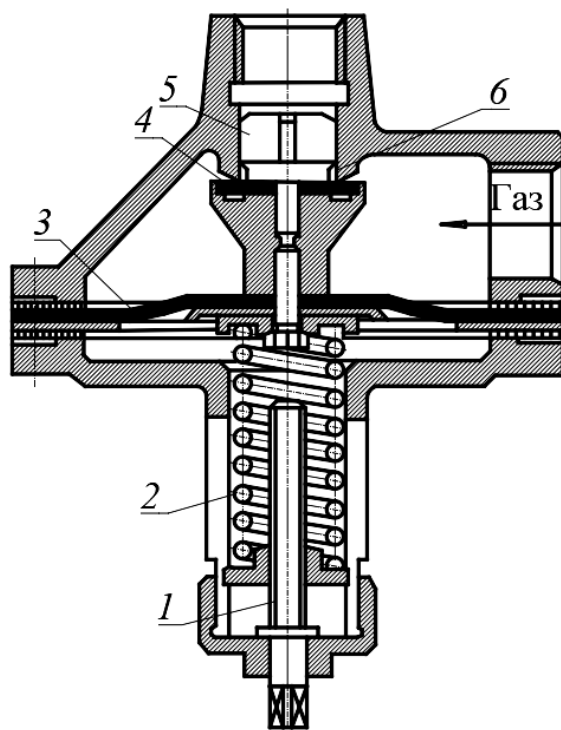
Запобіжно-скидний клапан ЗСК:
